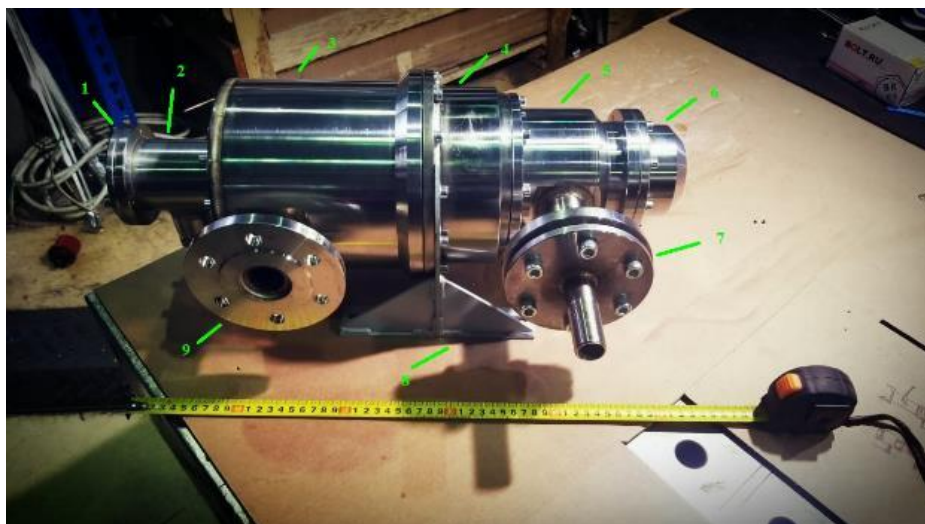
Внешний вид опытного образца роторного ДГА в сборе. 1 – крышка электрической распределительной коробки; 2 – электрическая распределительная коробка; 3 – корпус генератора; 4 - переходной корпус (корпус муфты привода); 5 – корпус детандера; 6 – крышка полости шестерен синхронизатора вращения роторов; 7 – впускной патрубок; 8 – кронштейн крепления ДГА; 9 – выпускной патрубок.
